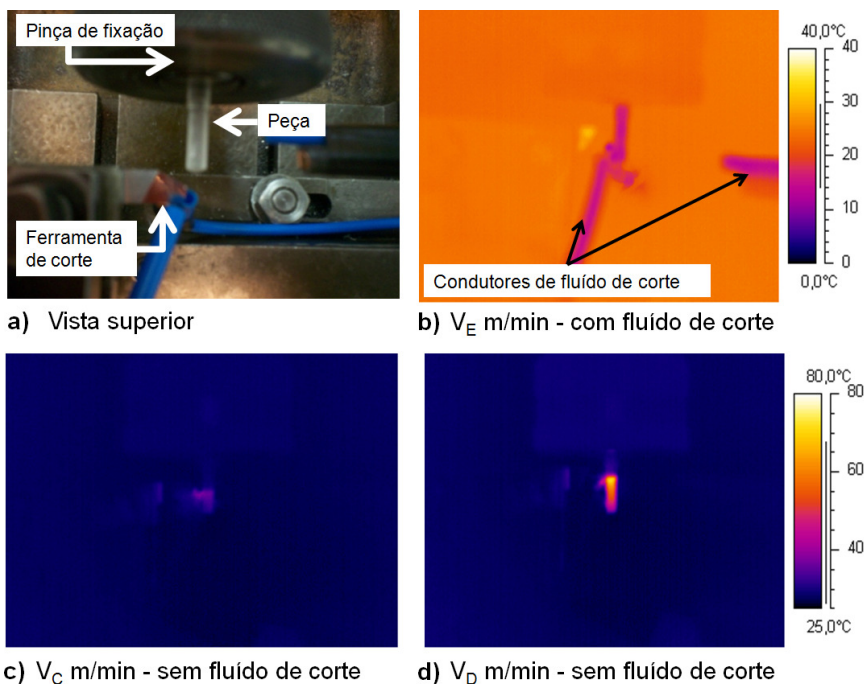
Imagens termográficas dos implantes durante a usinagem.
